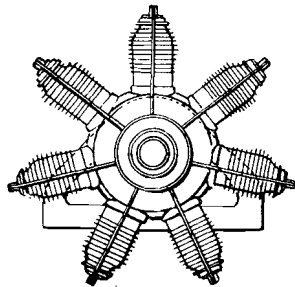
Umlaufmotor mit luftgekühlten Zylindern.
